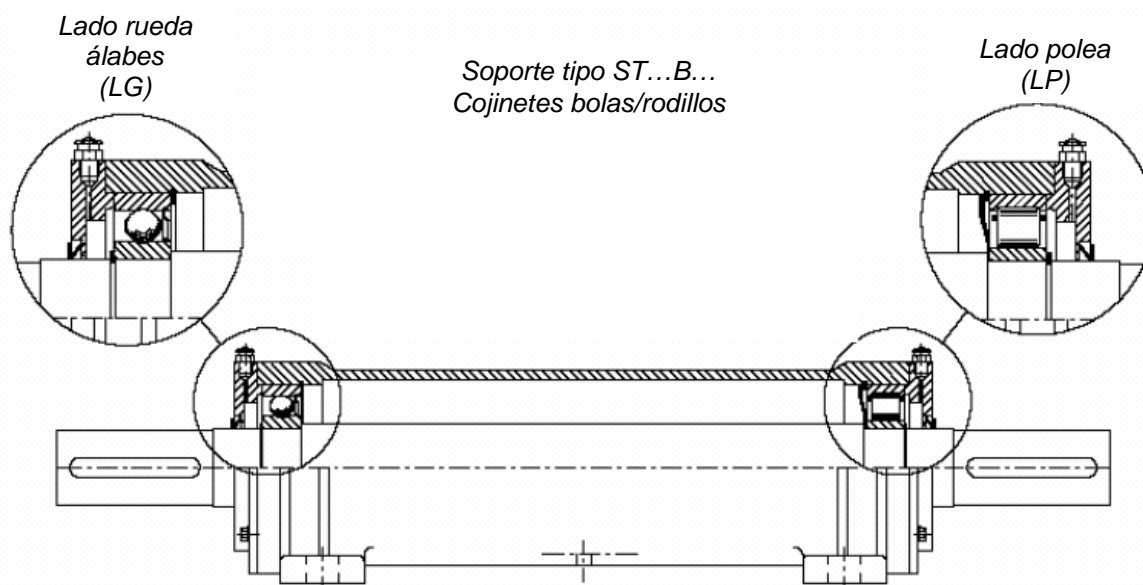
Soporte monobloque ST...B... con cojinete radial de bolas por el lado de la rueda de álabes y de rodillos por el lado de la transmisión
